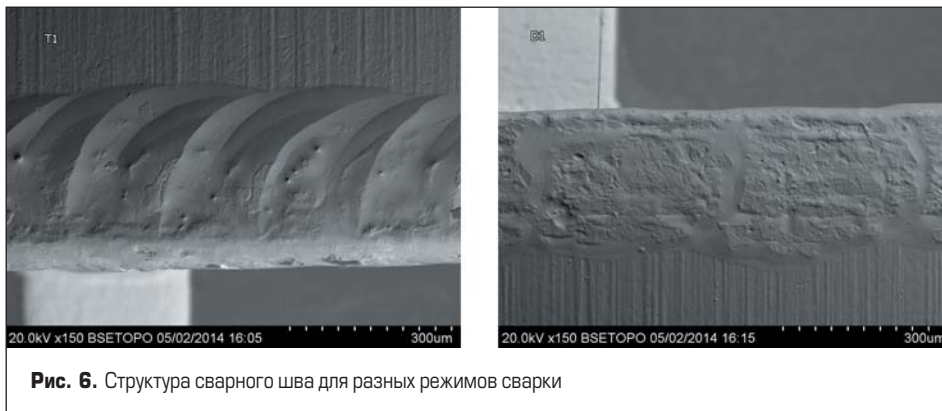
Структура сварного шва для разных режимов сварки
